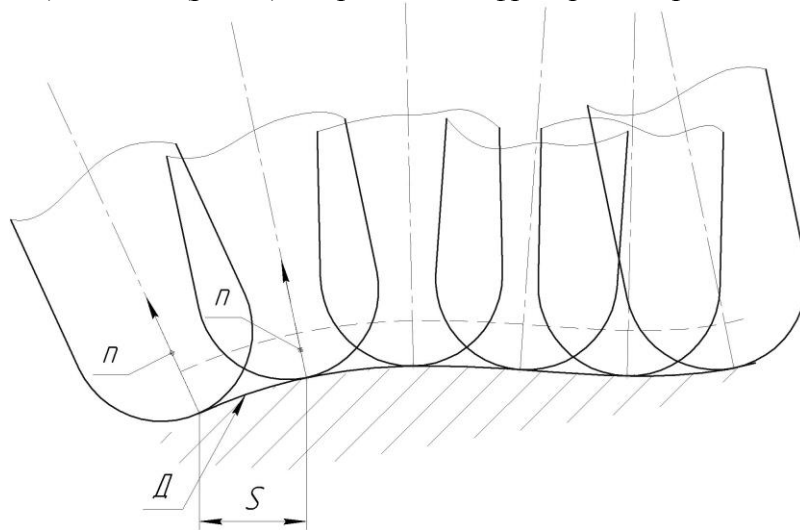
Схема обробки на 5-ти координатних фрезерних станках з ЧПК
